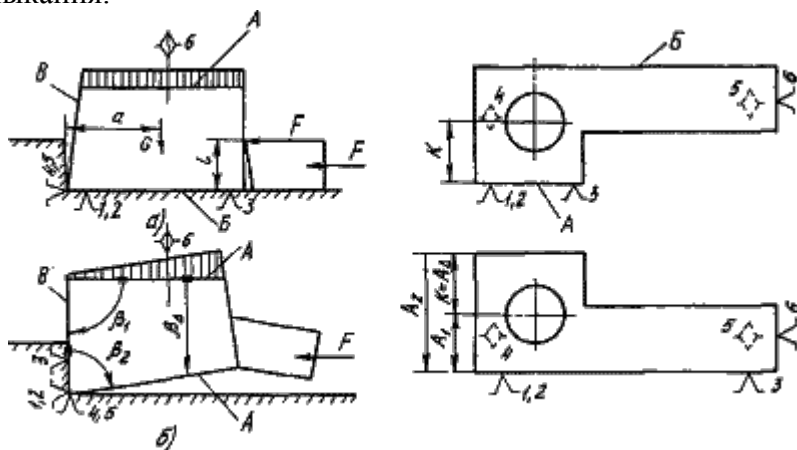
Смена баз у заготовок: а) неорганизованная, б) организованная
